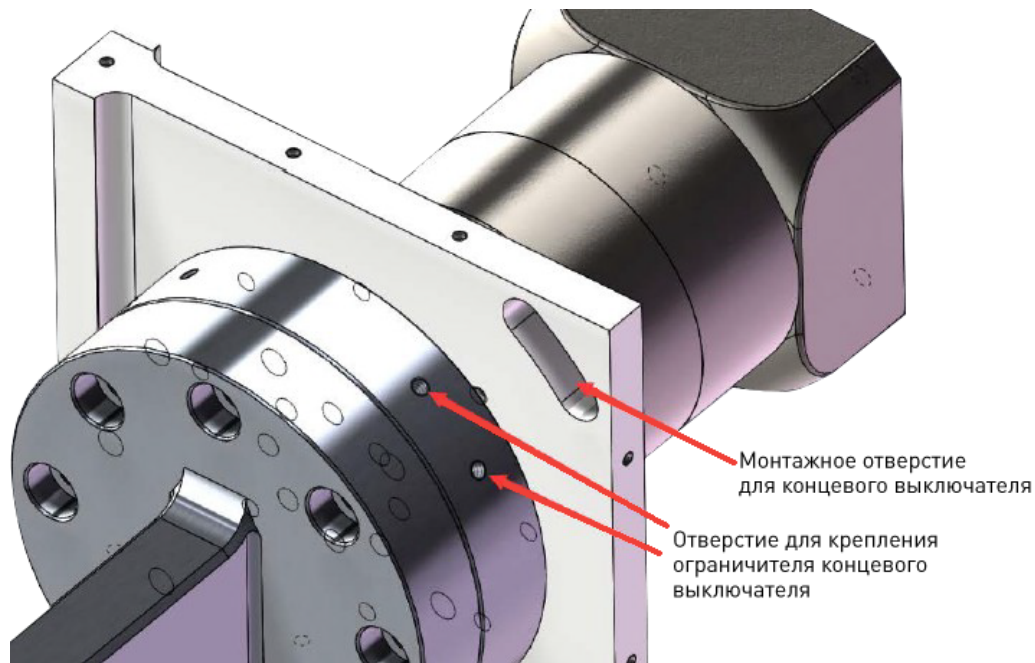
Установка концевых выключателей для оси поворота влево-вправо.
